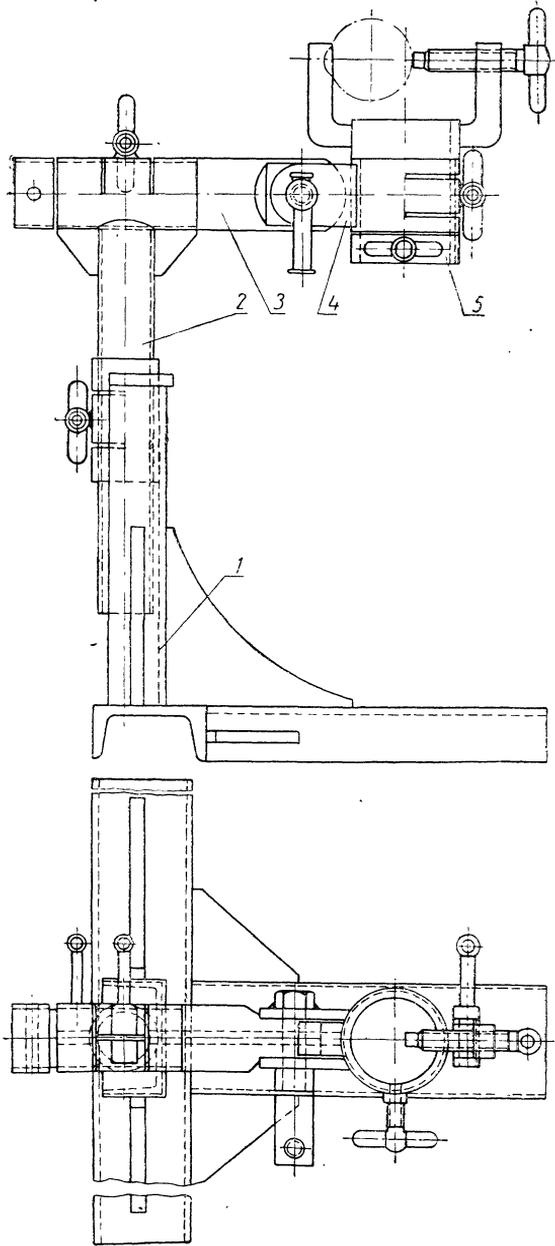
Приспособление для сварки траверсы вилки шасси.
